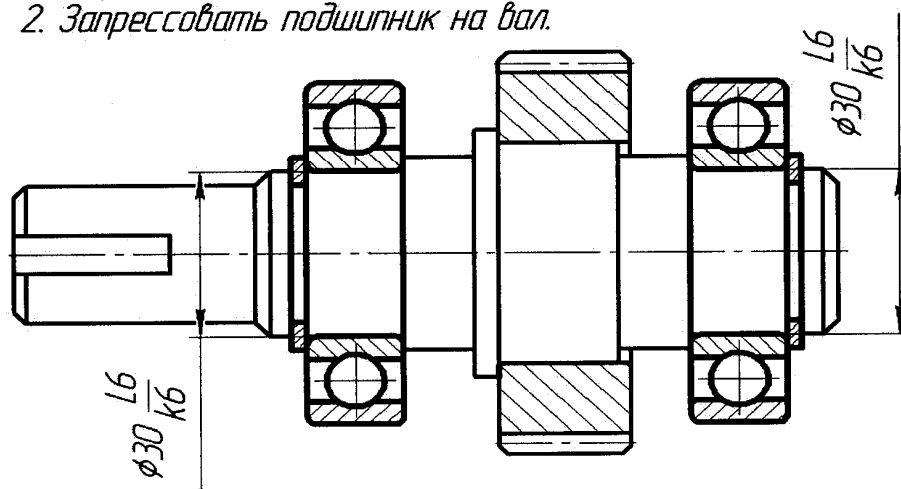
Пример графического изображения операции сборки первичного вала
